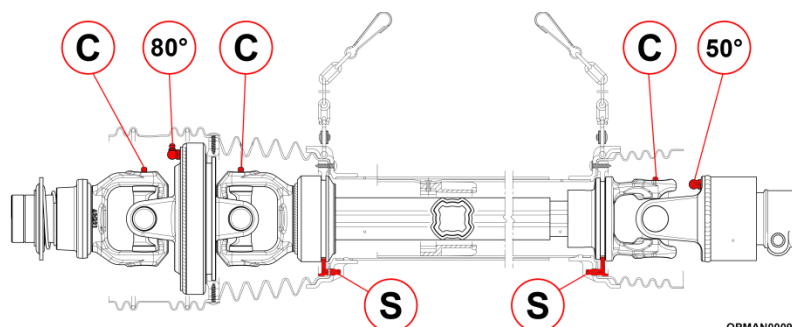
Emplacements des points de graissage d'arbre d'entrée de Multicut
